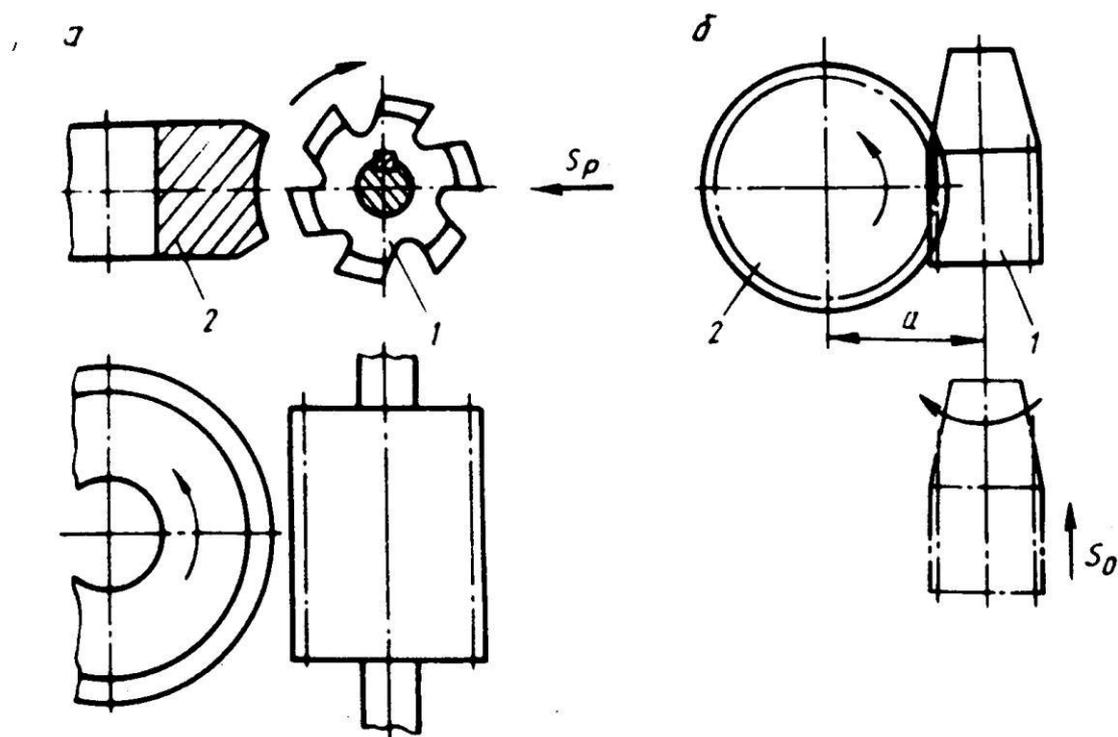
Схемы нарезания червячных колес червячной фрезой
